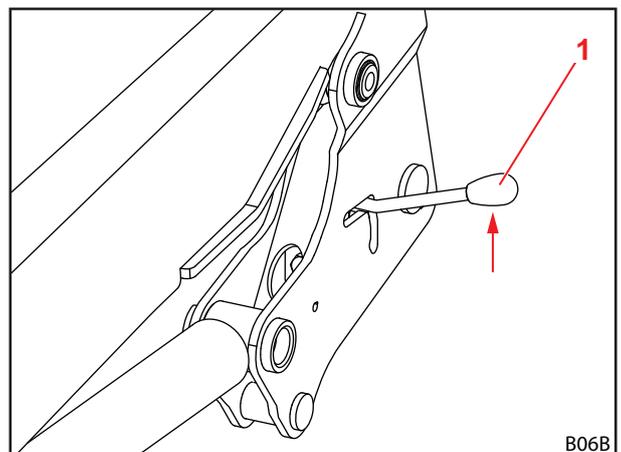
Apertura del dispositivo di blocco del caricatore frontale
